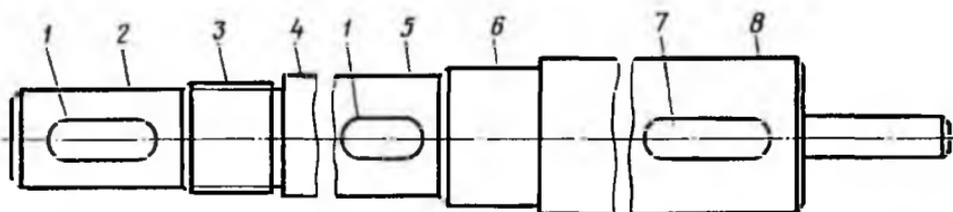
Схема центрального вала зернового комбайна с указанием дефектов
